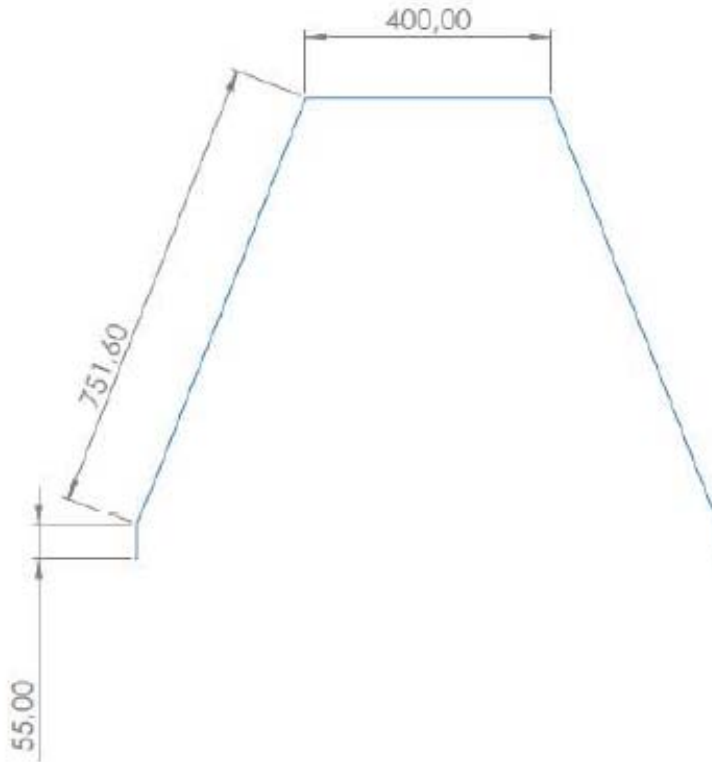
Dimensioni del carrello d'atterraggio [3].
